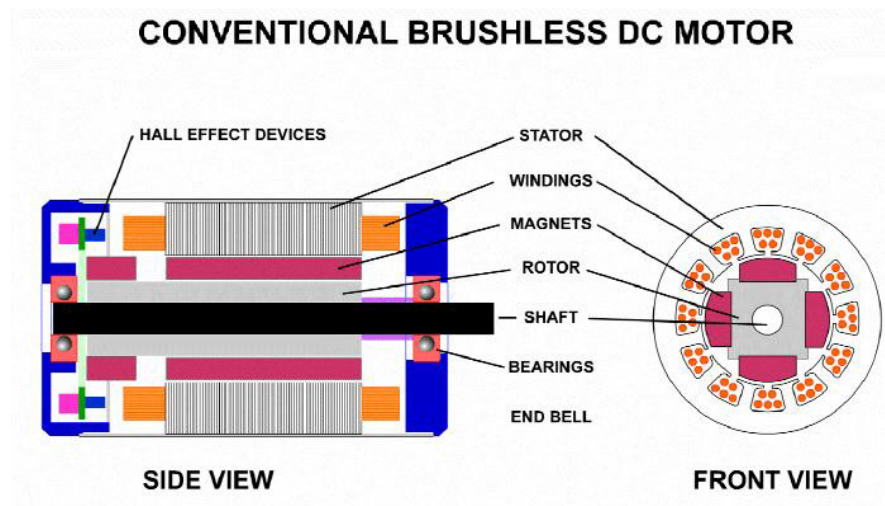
Despiece de Motor Brushless DC (Ref. [10])
